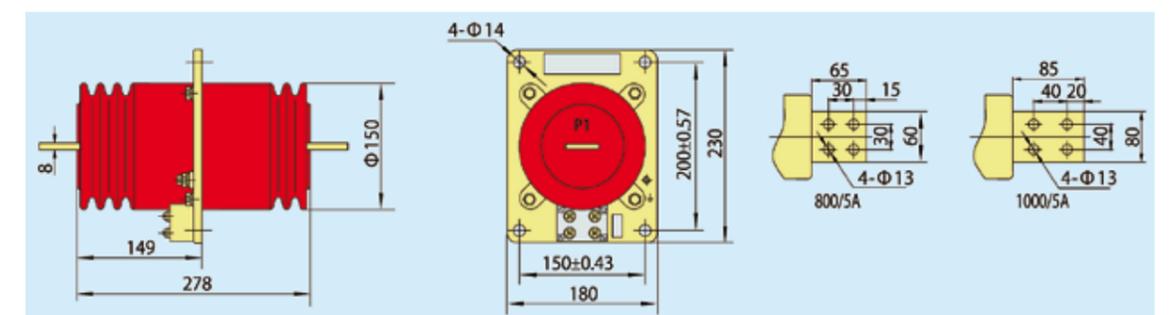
Внешний вид и размеры трансформатора тока LA-10(Q) 800~1000 А
